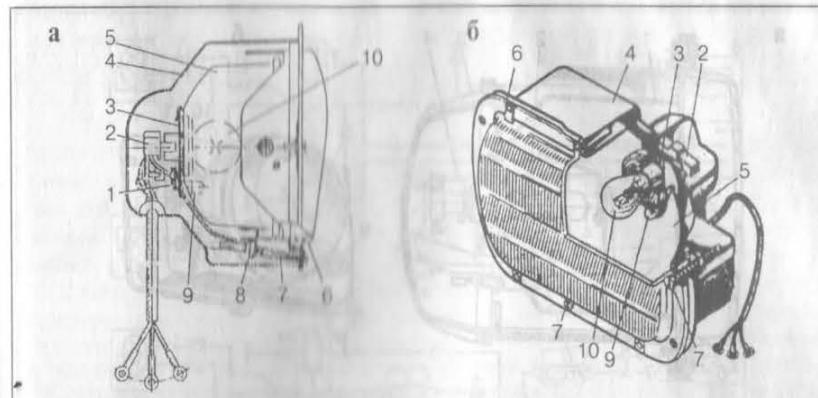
Прямоугольная фара: а - устройство; б - внешний вид. 1 - контактная пластина; 2 - соединительная колодка; 3 - металлическая пластина; 4 - пластмассовый кожух; 5 - отражатель; 6 - корпус; 7 - регулировочный винт; 8 - пластмассовая гайка; 9 - лампа габаритного огня; 10 - двухнитевая лампа
